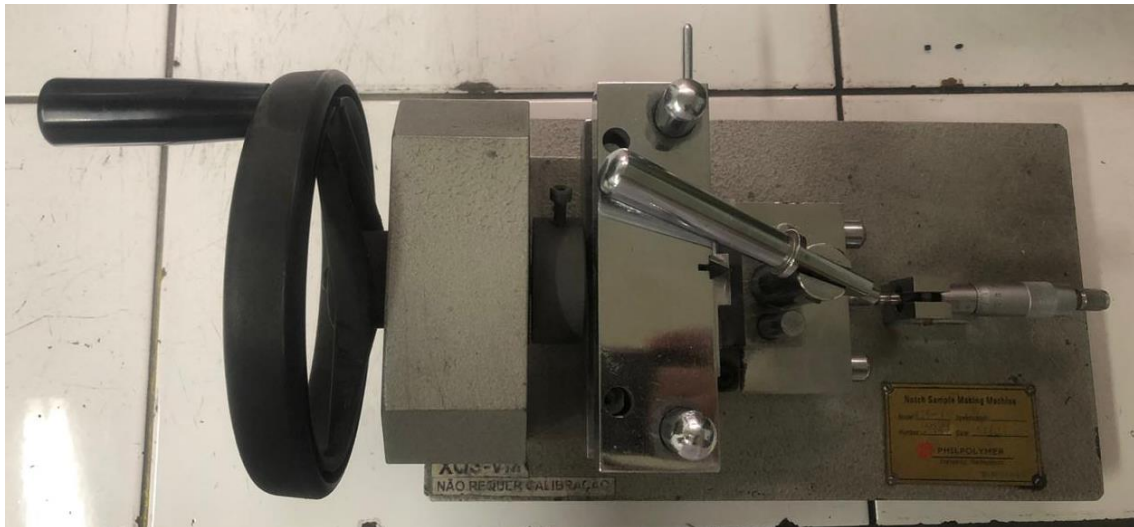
Máquina "Notching Sample Making Machine" usada para entalhar a amostra antes do teste de impacto
